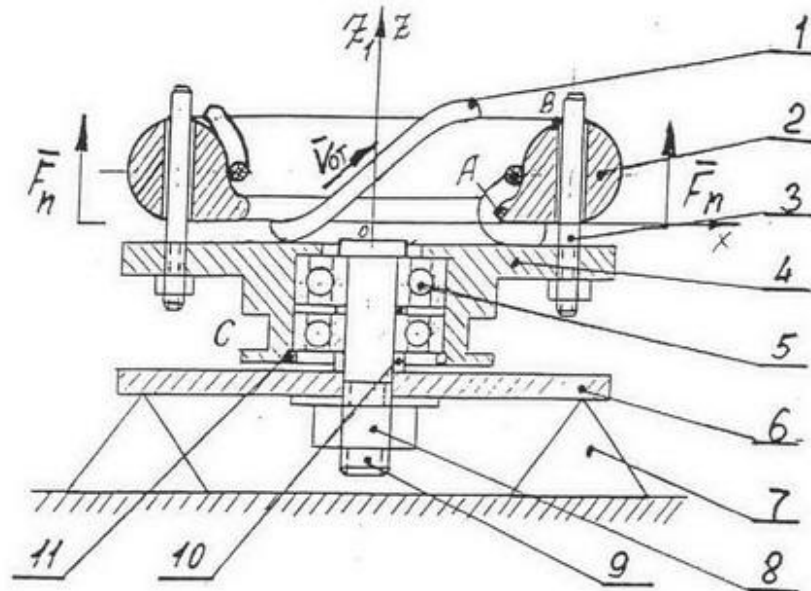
Тороидальный летательный аппарат-инерцид конструкции В.И. Докучаева (1996г). Сборочный чертёж
